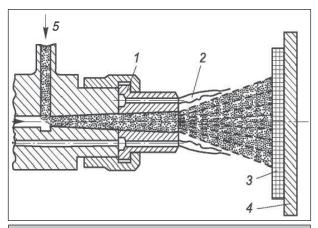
Схема порошкового распылителя: 1— газовое сопло; 2— кольцевое пламя; 3— покрытие; 4— подложка; 5— порошок
